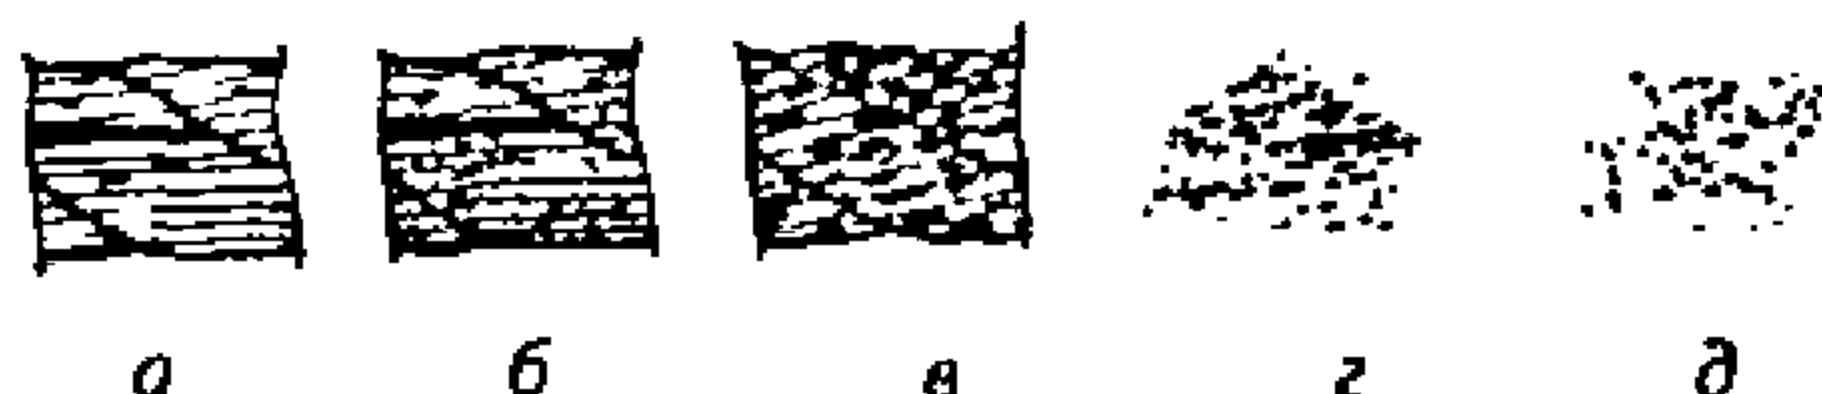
Поверхностная коррозия проволок каната крестовой свивки:
